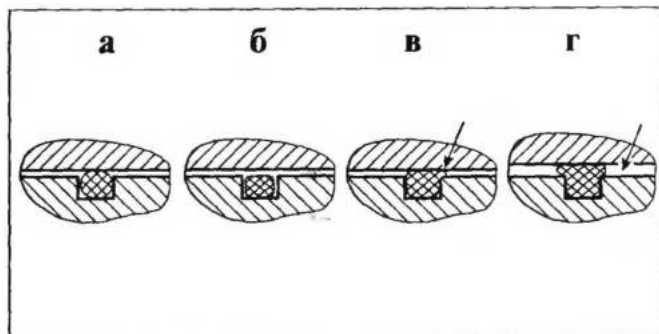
Типичные ошибки при сборке деталей с уплотнительными резиновыми кольцами:
